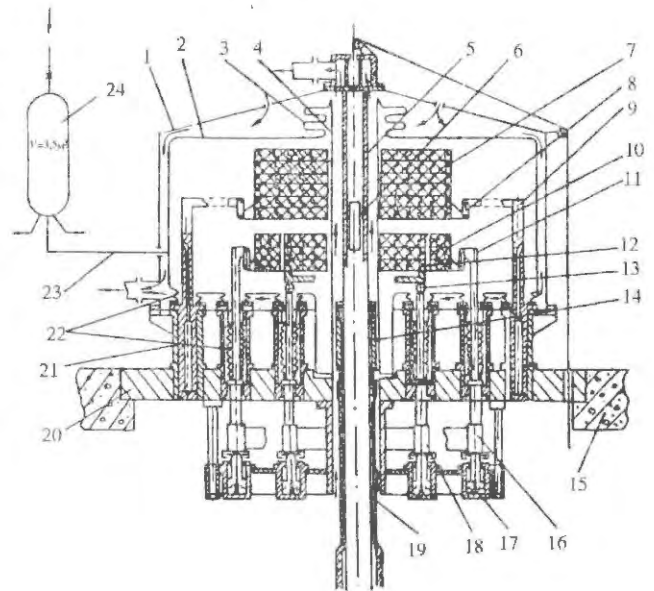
Конструктивная схема реактора БИГР [4]: 1 – кожух охлаждения; 2 – герметичный корпус; 3 – компенсатор теплового расширения корпуса; 4 – центральная труба корпуса; 5 – осевой канал; 6 – контейнер; 7 – неподвижная часть АЗ; 8 – шарнирная подвеска; 9 – опорная колонна неподвижной части АЗ; 10 – блок точного регулирования реактивности; 11 – штанга блока точного регулирования; 12 – блок грубого регулирования реактивности; 13 – опорный ролик блока грубого регулирования; 14 – импульсный блок; 15 – железобетонное перекрытие; 16, 18 – траверсы блоков регулирования реактивности; 17 – демпфер масляный; 19 – толкатель импульсного стержня; 20 – плита защитная; 21 – опорная колонна; 22 – сильфоны; 23 – газопровод; 24 – ресивер
